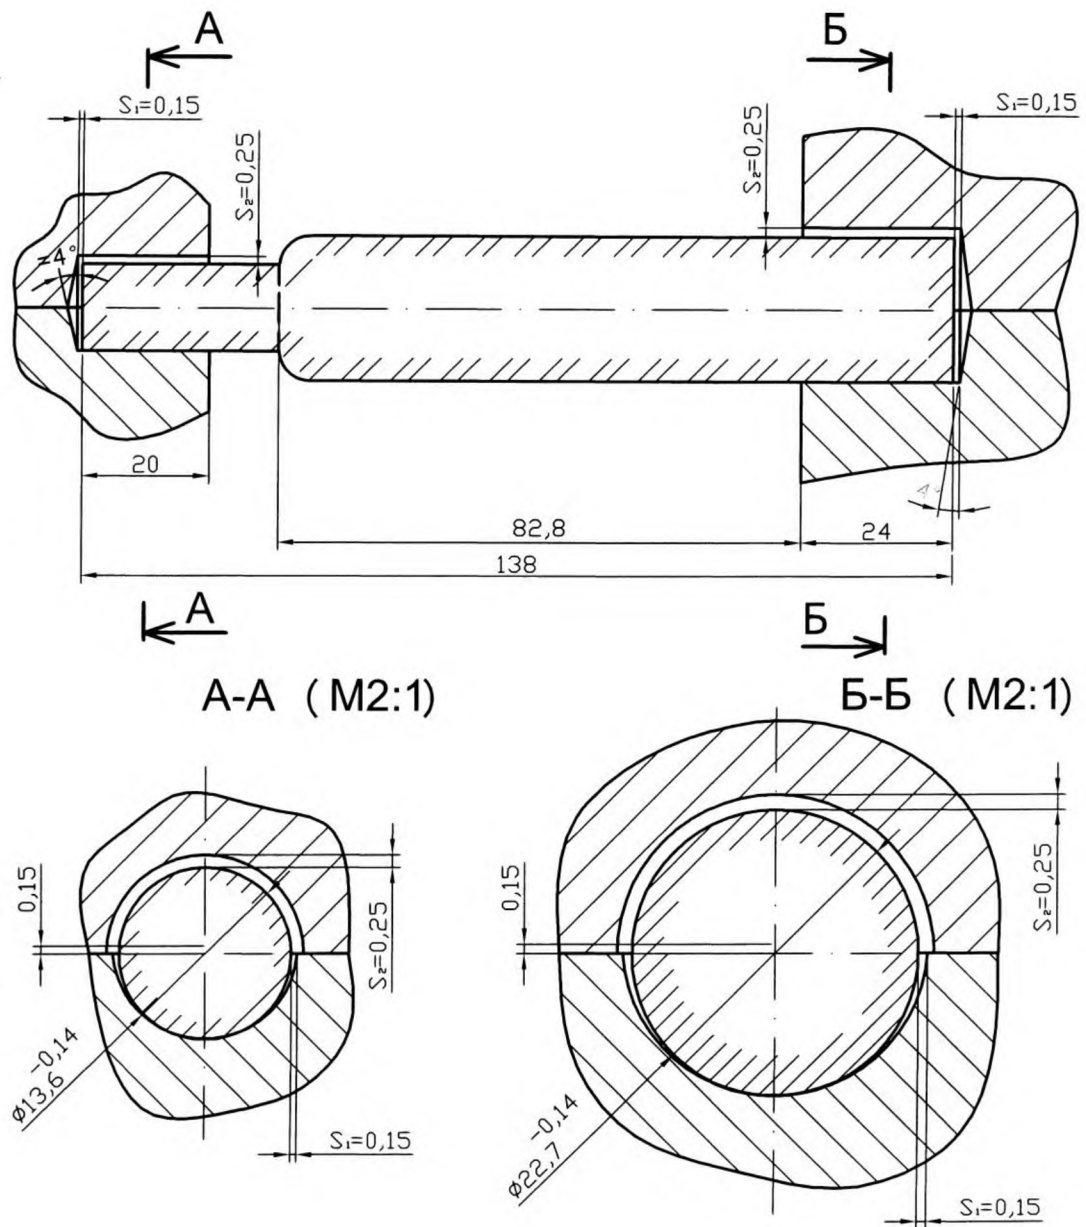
Стержень и знаки литейной формы отливки «Суппорт»
